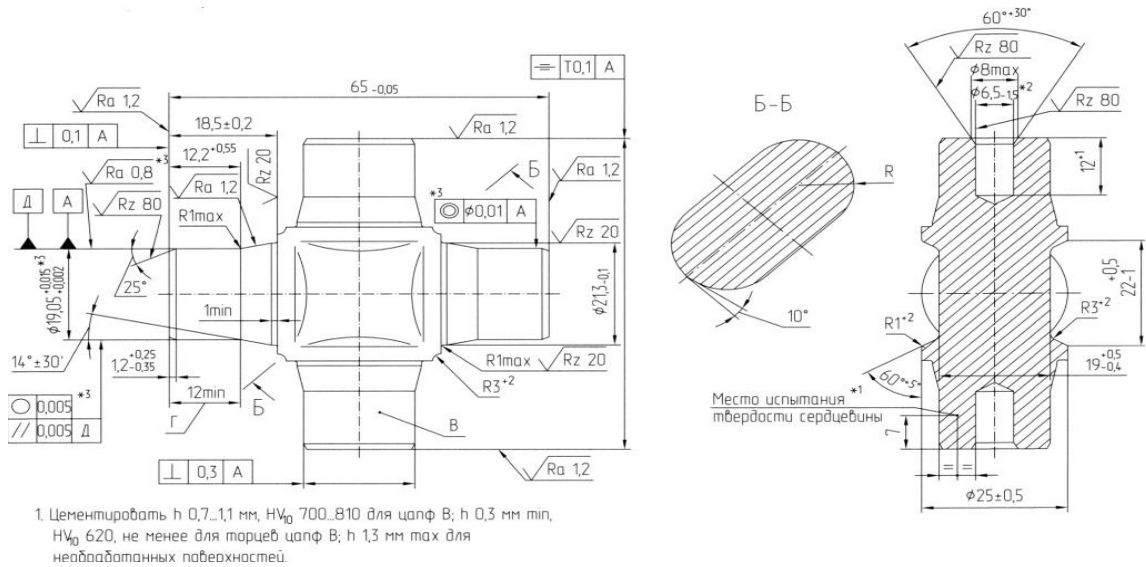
Чертеж заготовок для экспериментов
